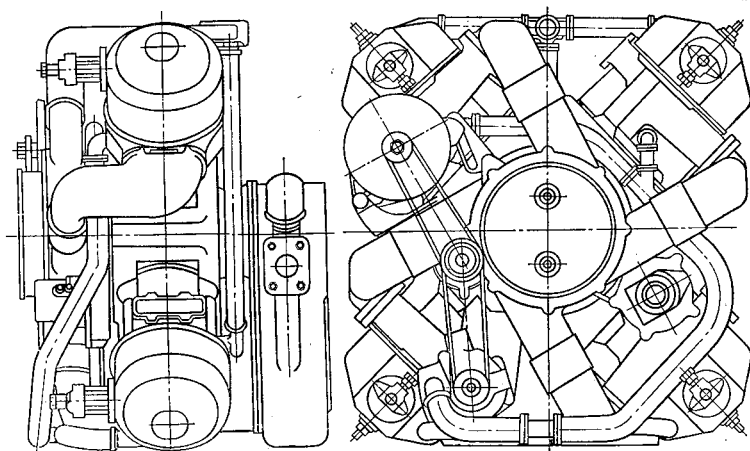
Внешний вид двигателя Дина-Стар мощностью 100 л. с.
